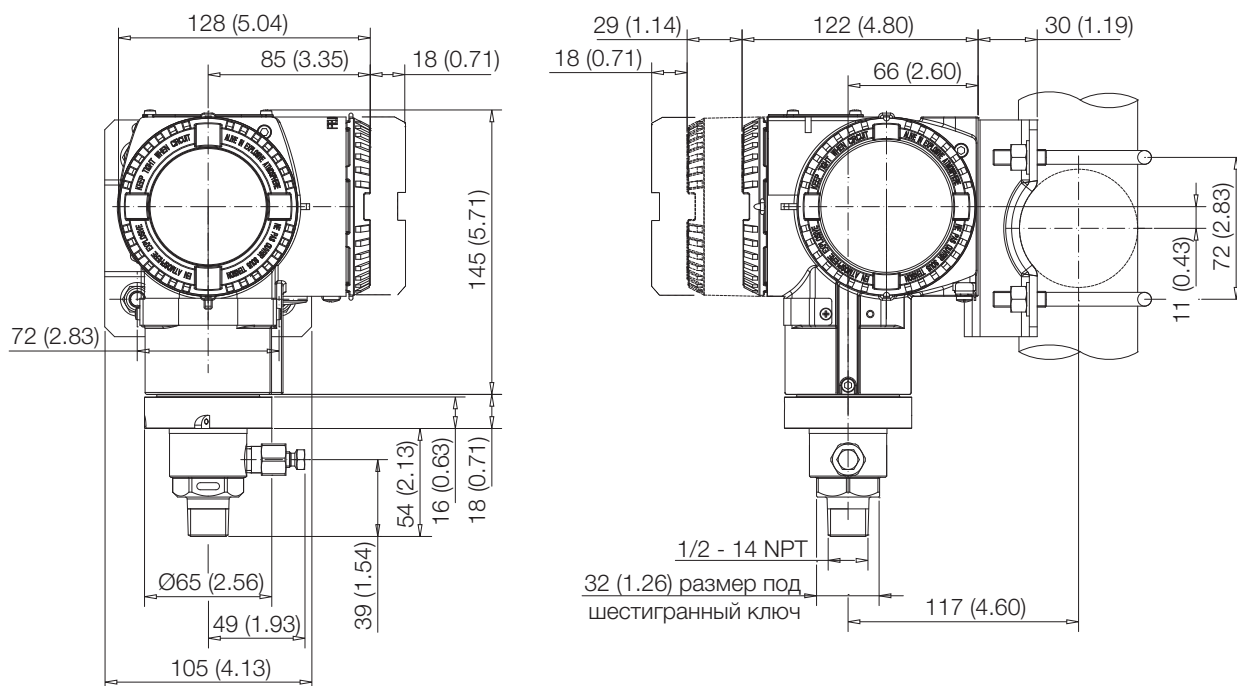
Модель 266N или P-образный устойчивый к перегрузкам датчик 266N Hi с корпусом по стандарту DIN установленный на двухдюймовой трубе с помощью дополнительного кронштейна (B7 - нержавеющая сталь 316L)
